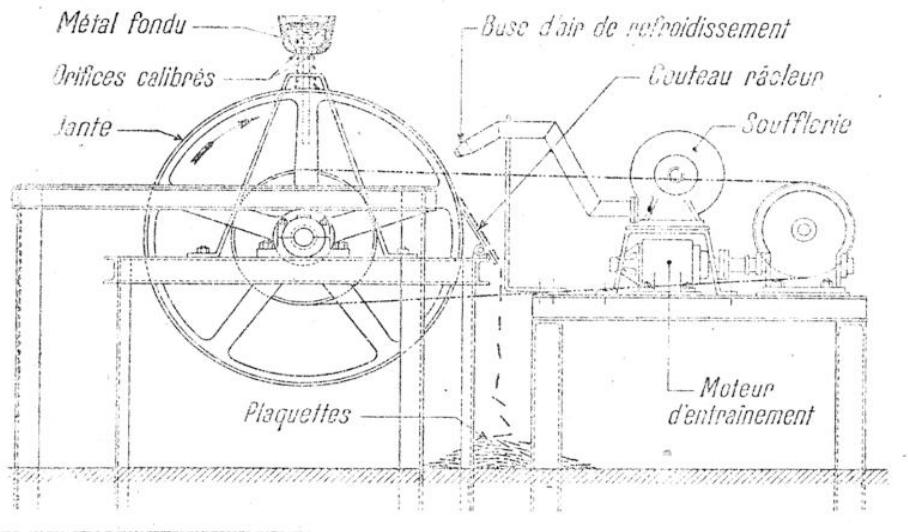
MACHINE A COULER LES PLAQUETTES-ÉBAUCHES POUR LA FABRICATION DES POU DRES MÉTALLIQUES
